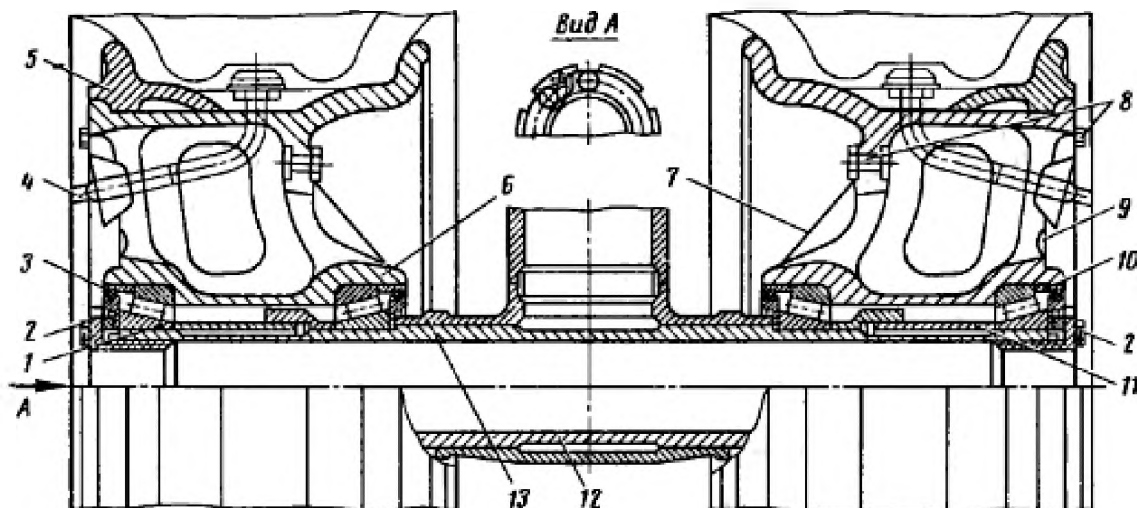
Колесо передней стойки шасси вертолета Ми-8 [5]:
